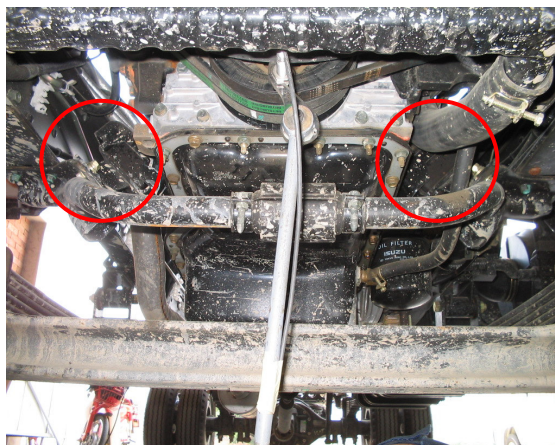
Montaje del motor NPR 4HG1T en el chasis.
